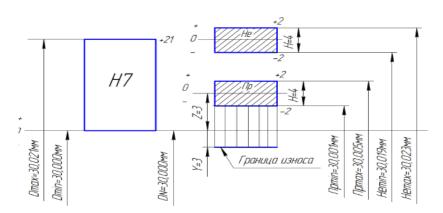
Схема расположения полей допусков калибров для контроля отверстия 30*H*7
